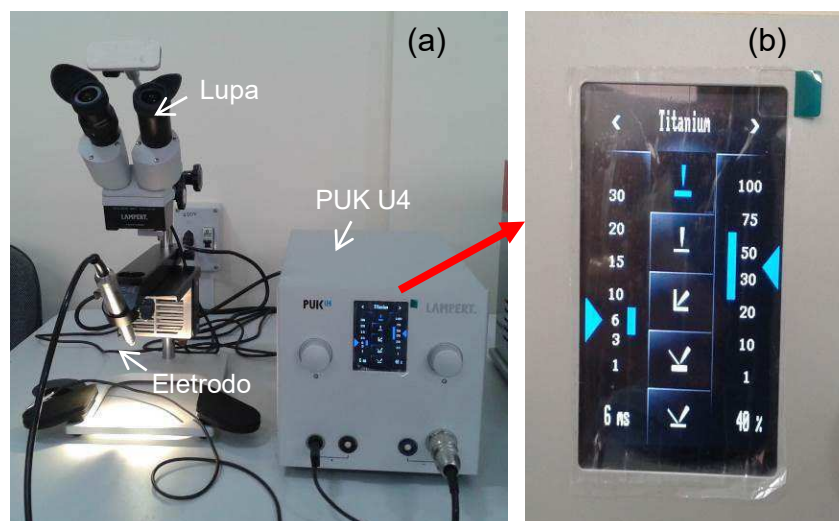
Equipamento de soldagem PUK U4 com lupa binocular acoplada. (a) Visão geral do equipamento. (b) Detalhe da função para soldagem de titânio puro com pré-configuração de parâmetros (destacados pelas setas e faixa azul).
